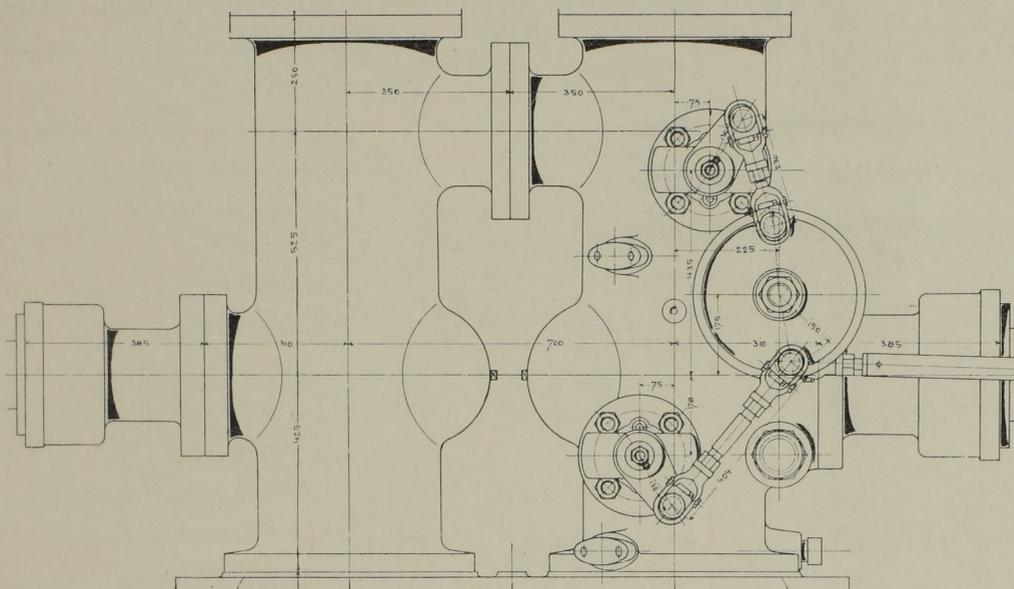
Seitenansicht und Pumpensteuerung. Massst. 1:5.
